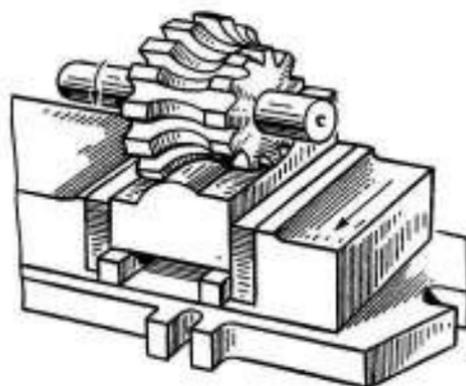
Фрезерование фасонной поверхности фасонной фрезой
